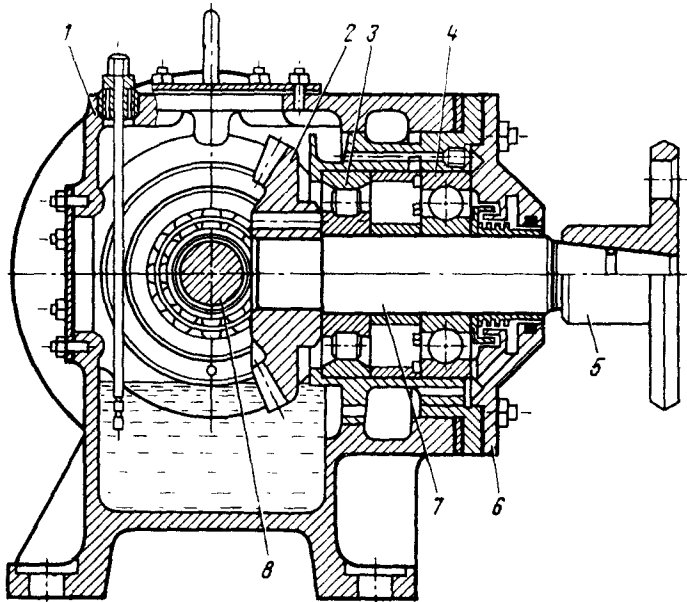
Редуктор вентилятора охлаждения тягового генератора:
